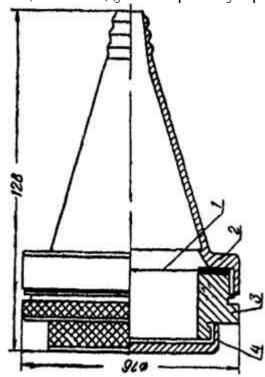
Металлический патрон для пылеулавливающего фильтра: 1 - фильтр, 2 - корпус, 3 - гайка, 4 - крышка.
